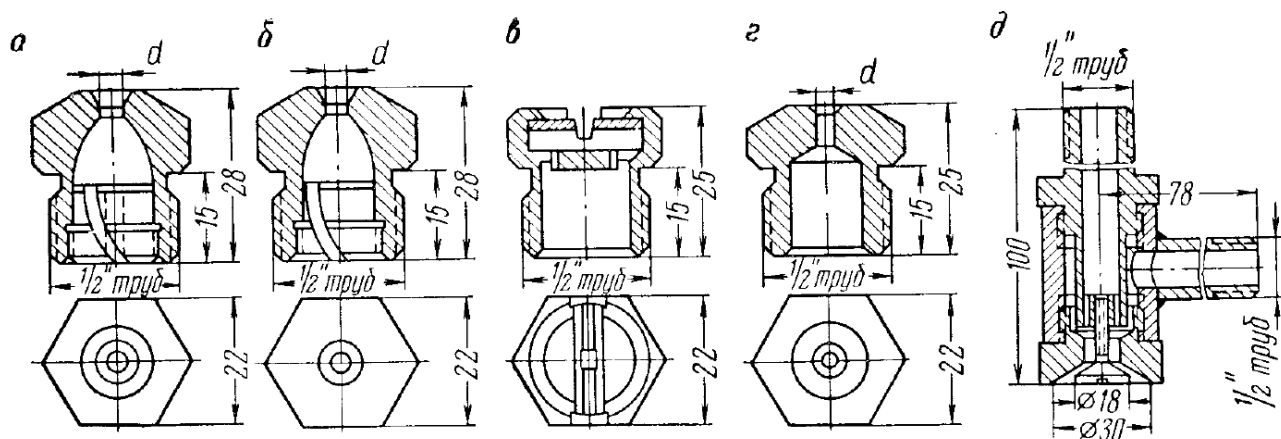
Конструкції форсунок для зрошення [15]: а – форсунки типу КФ; б – форсунка типу ЗФ; в – форсунки типу ПФ; г – насадки типу Н; д – пароводяні форсунки типу Ф-2
